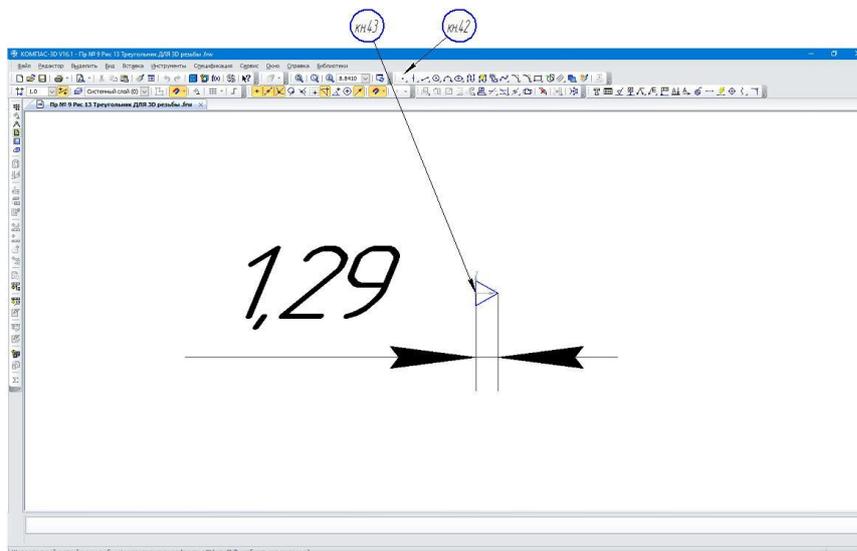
Эскиз треугольника (профиля метрической резьбы)
